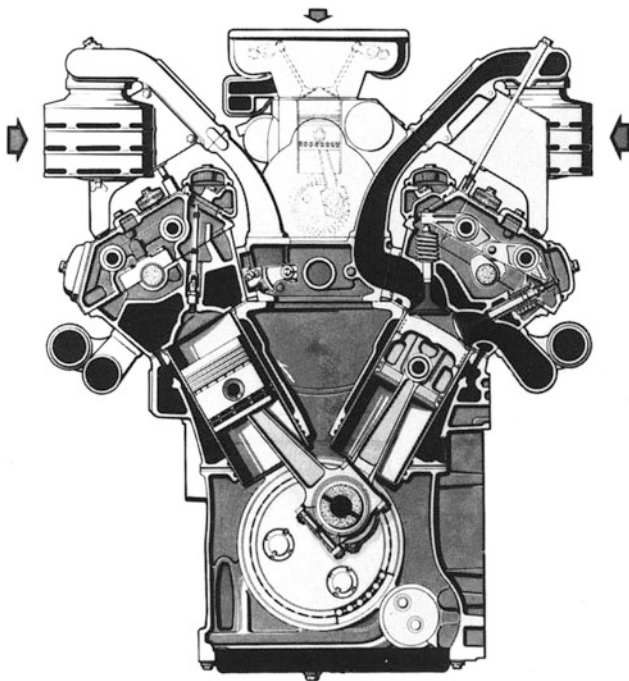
Querschnitt des Panzermotors HL 295 mit dem Hilfsmotor HL 11
